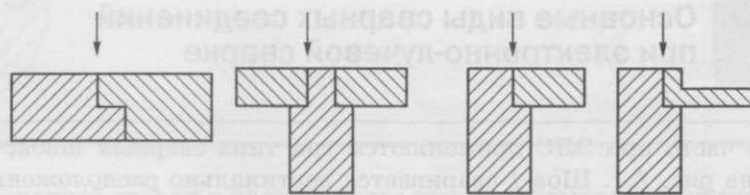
Схема пространственного расположения сварных швов при ЭЛС:
